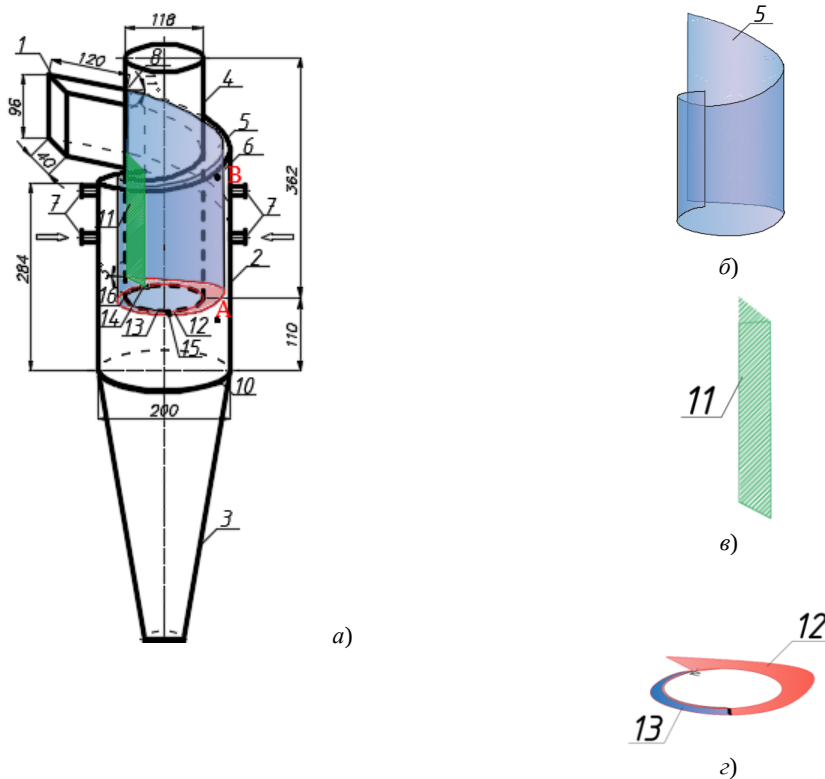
Схема конструкции циклона-фильтра: 1 – входной патрубок; 2 – цилиндрический корпус; 3 – коническое днище; 4 – выхлопная труба; 5 (б) – фильтровальный материал; 6 – металлический каркас; 7 – продувочные штуцера; 8 – торец циклона; 9 – заслонка; 10 – детали крепежа; 11 (б) – поперечный фильтр; 12 (с) – горизонтальный фильтр, тканая часть; 13 – горизонтальный фильтр, металлическая часть; 14 – пластина с пружиной; 15 – стержень с кольцами; 16 – складывающийся фильтр; А, В – порты ввода термоанометра
